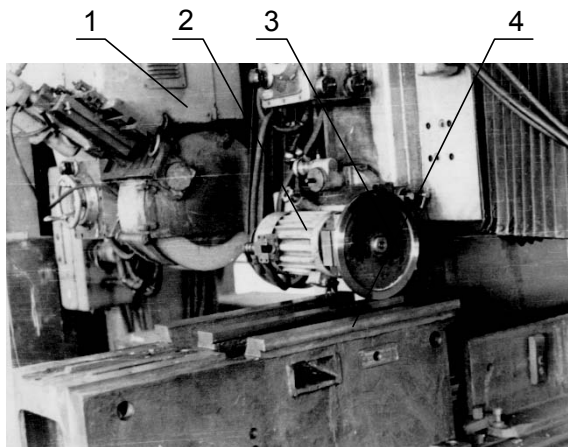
Загальний вигляд установки для фрикційного зміцнення напрямних станин: 1 - поздовжньо-шліфувальний верстат; 2 - поворотна головка; 3 - зміцнювальний інструмент-диск; 4 - напрямна станини.
